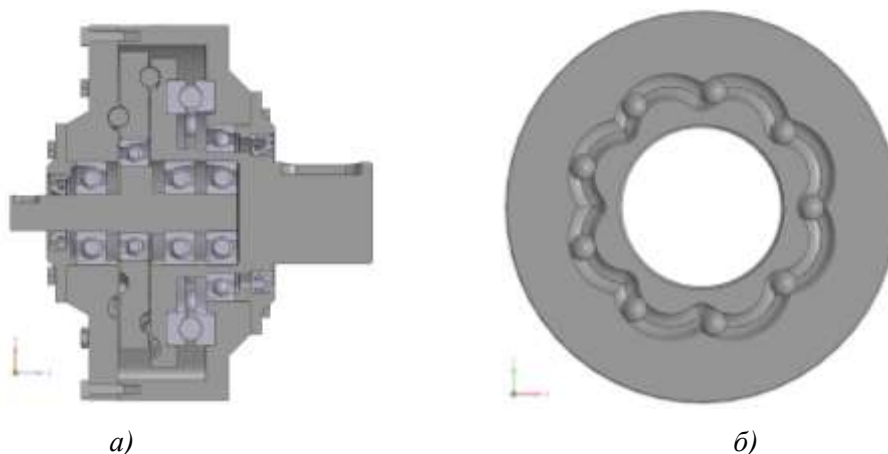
CAD-модель: а – редуктора; б – сателлита с промежуточными телами качения
